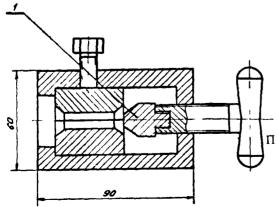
Приспособление для сборки скользящих контактов камеры:
